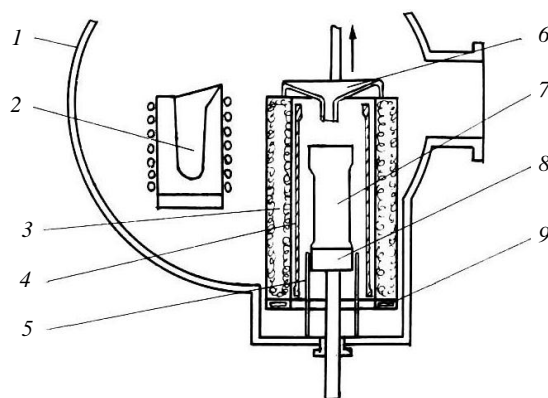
Принципиальная схема конструкции печи УВНЭС-2: 1 – вакуумная камера; 2 – плавильный тигель; 3 – печь подогрева форм; 4 – нагреватель; 5 – опорный стакан; 6 – заливочная воронка; 7 – керамическая форма; 8 – кристаллизатор; 9 – кольцевой холодильник
